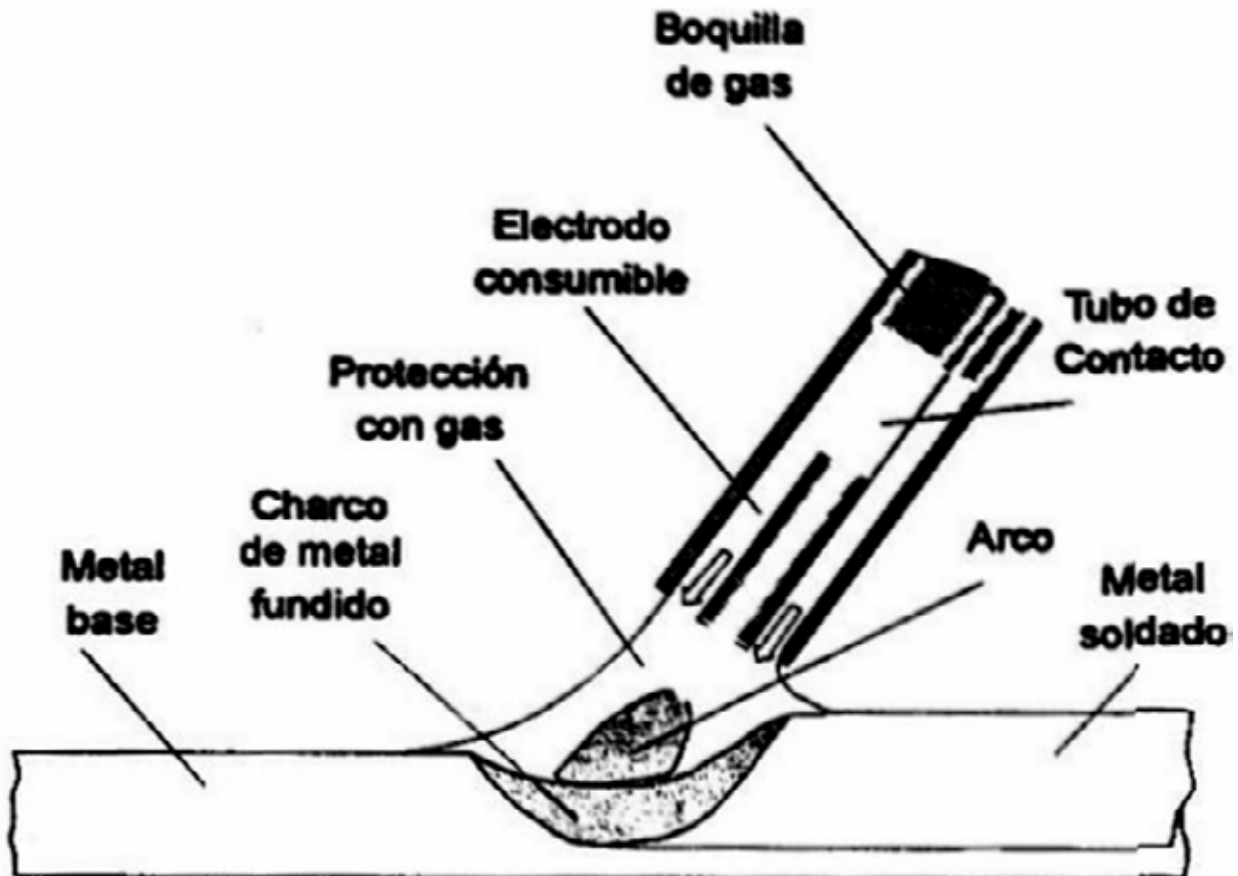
Soldadura de Arco Eléctrico con Protección de Gas (CMAW)
